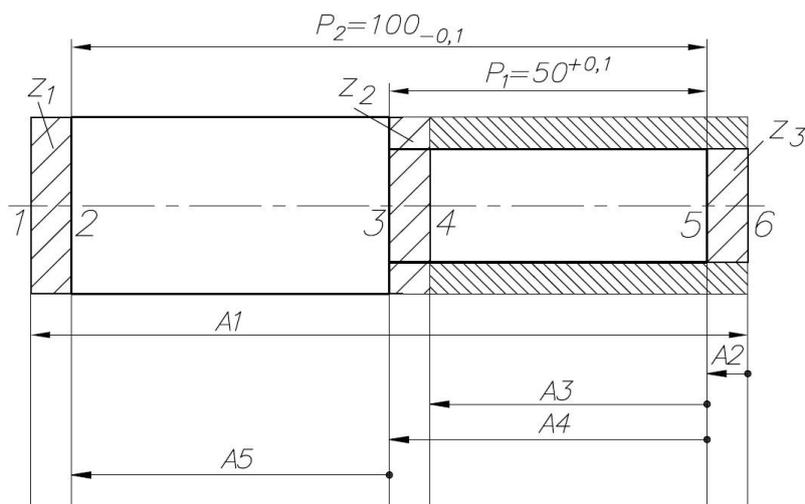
Размерная схема 7 варианта ТП для заготовки «пруток»
